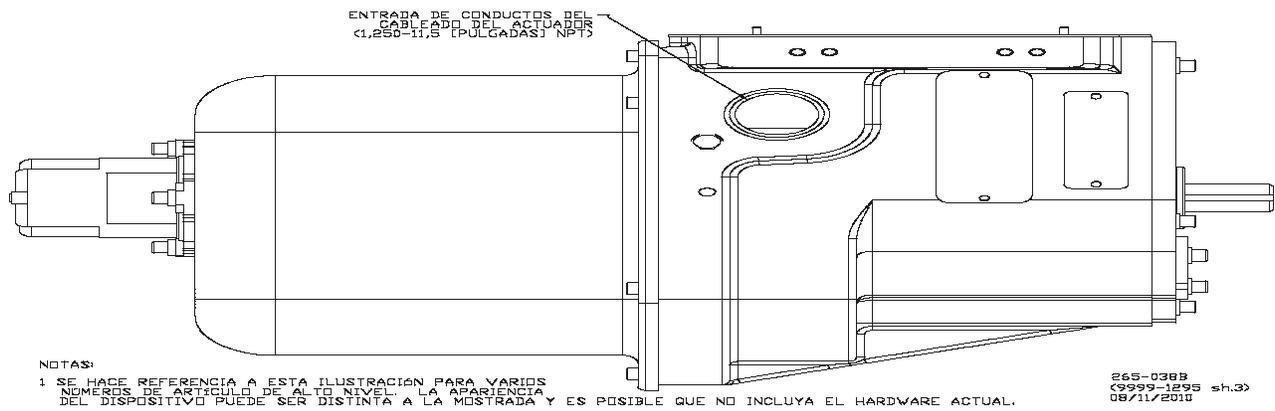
Diagrama de cableado del actuador de RVP-200 (caja de engranajes)
